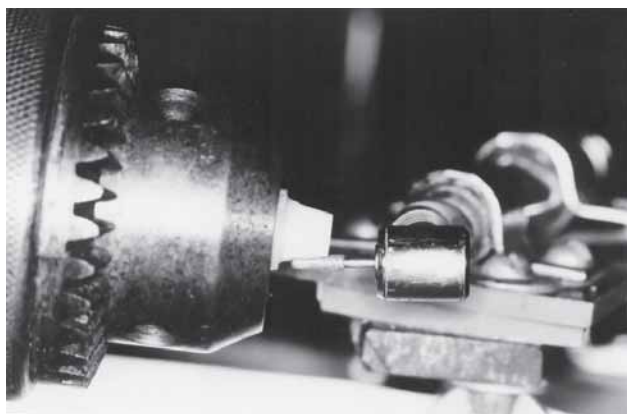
Preparo da parede axial com o dente incluído em resina acrílica e posicionado no torno.
